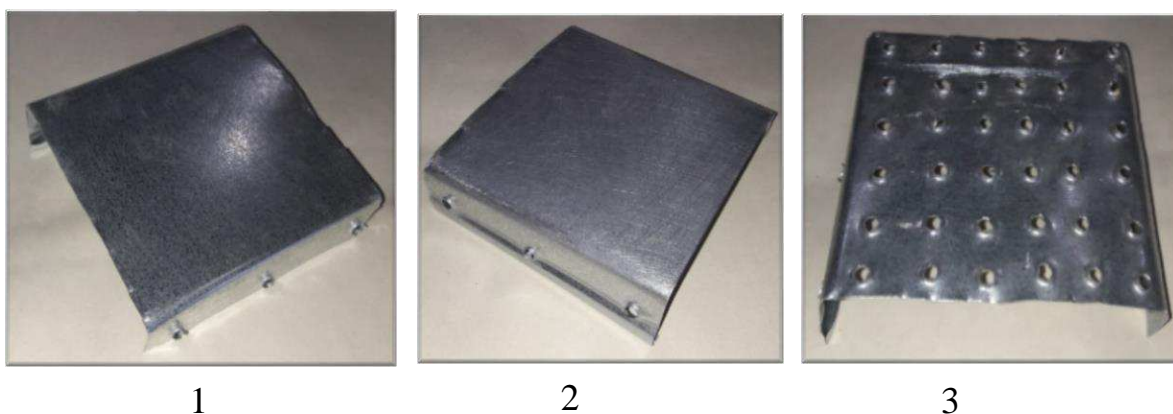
образцы, изготовленные из стального оцинкованного листа
